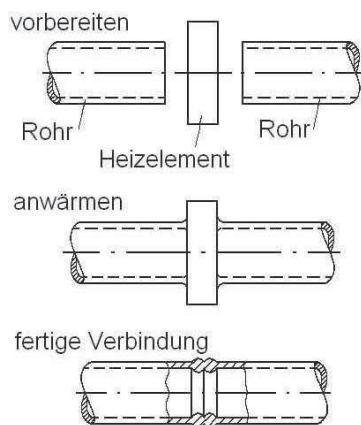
Prinzip des Heizelementstumpfschweißens am Beispiel Rohr.
